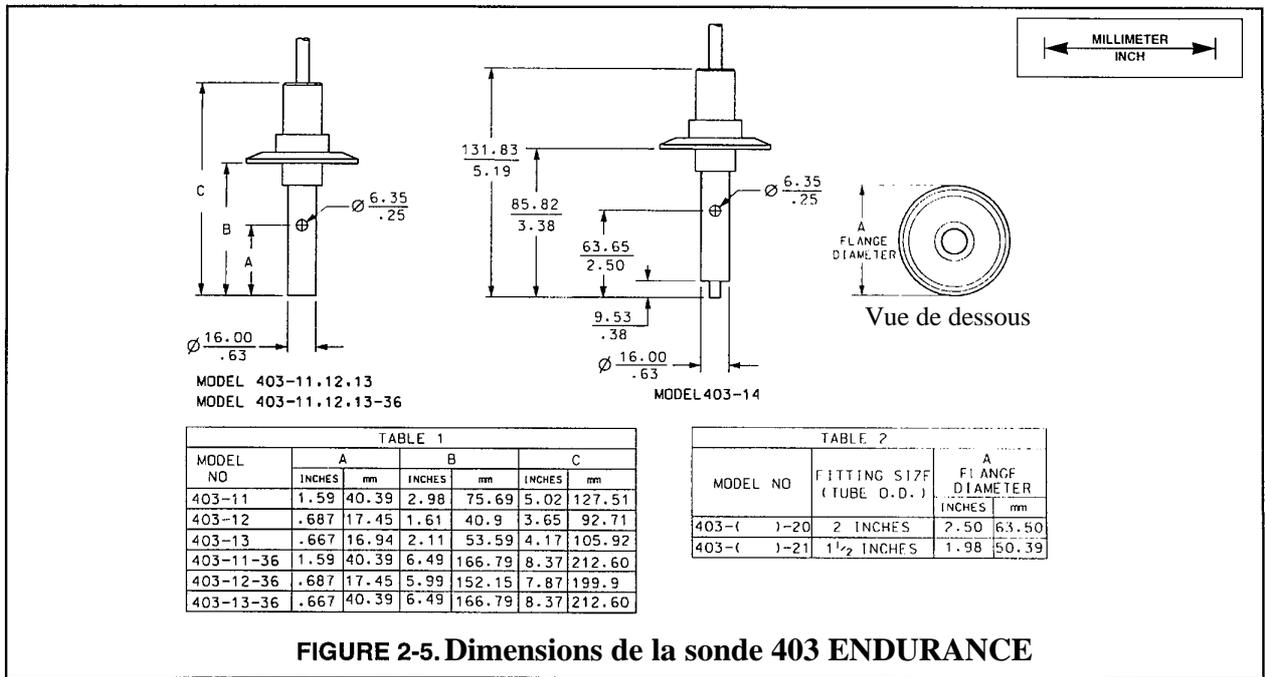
Dimensions de la sonde 403 ENDURANCE
